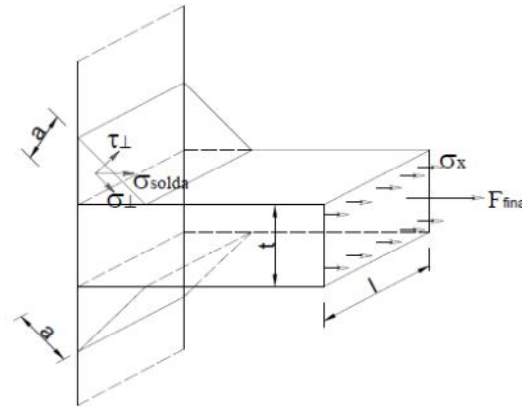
Cordão de soldadura de ângulo e lateral
